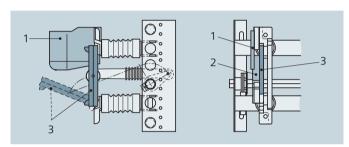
выключатель-разъединитель 3CJ2: (1) плоская автогазовая дугогасящая камера, (2) контактный нож, (3) вспомогательный нож
